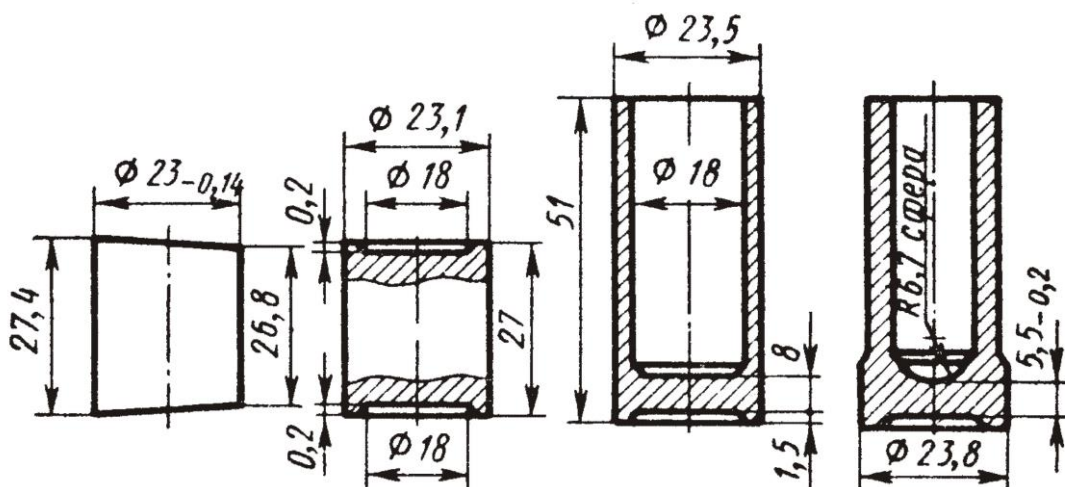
Переходы при штамповке корпуса толкателя из стали 15Х
